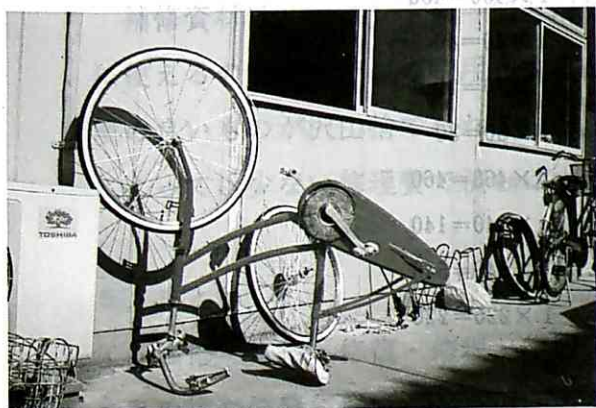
塗装後の天日干し (081, 81) = 写真-8 組立て作業
